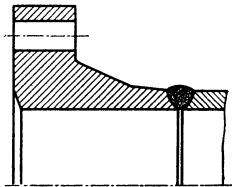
Hochdruck-Vorschweißflansch mit Eindrehung für Linsendichtung.
